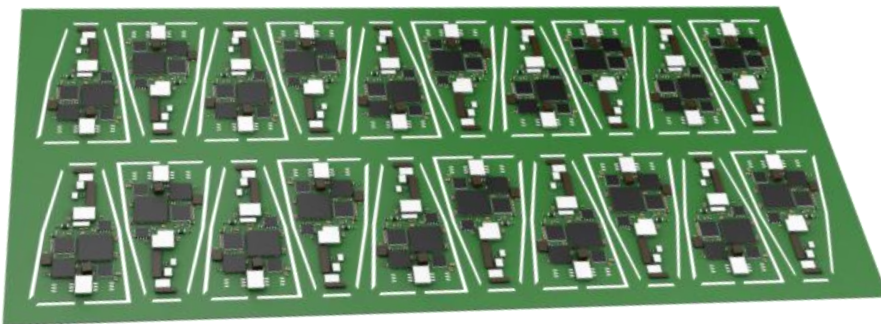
Baugruppen-Nutzen mit beidseitig bestückten Baugruppen; Bildaufnahmezeit mit konventionellen Flat-Panel-Detektoren: ca. 160 Sekunden
